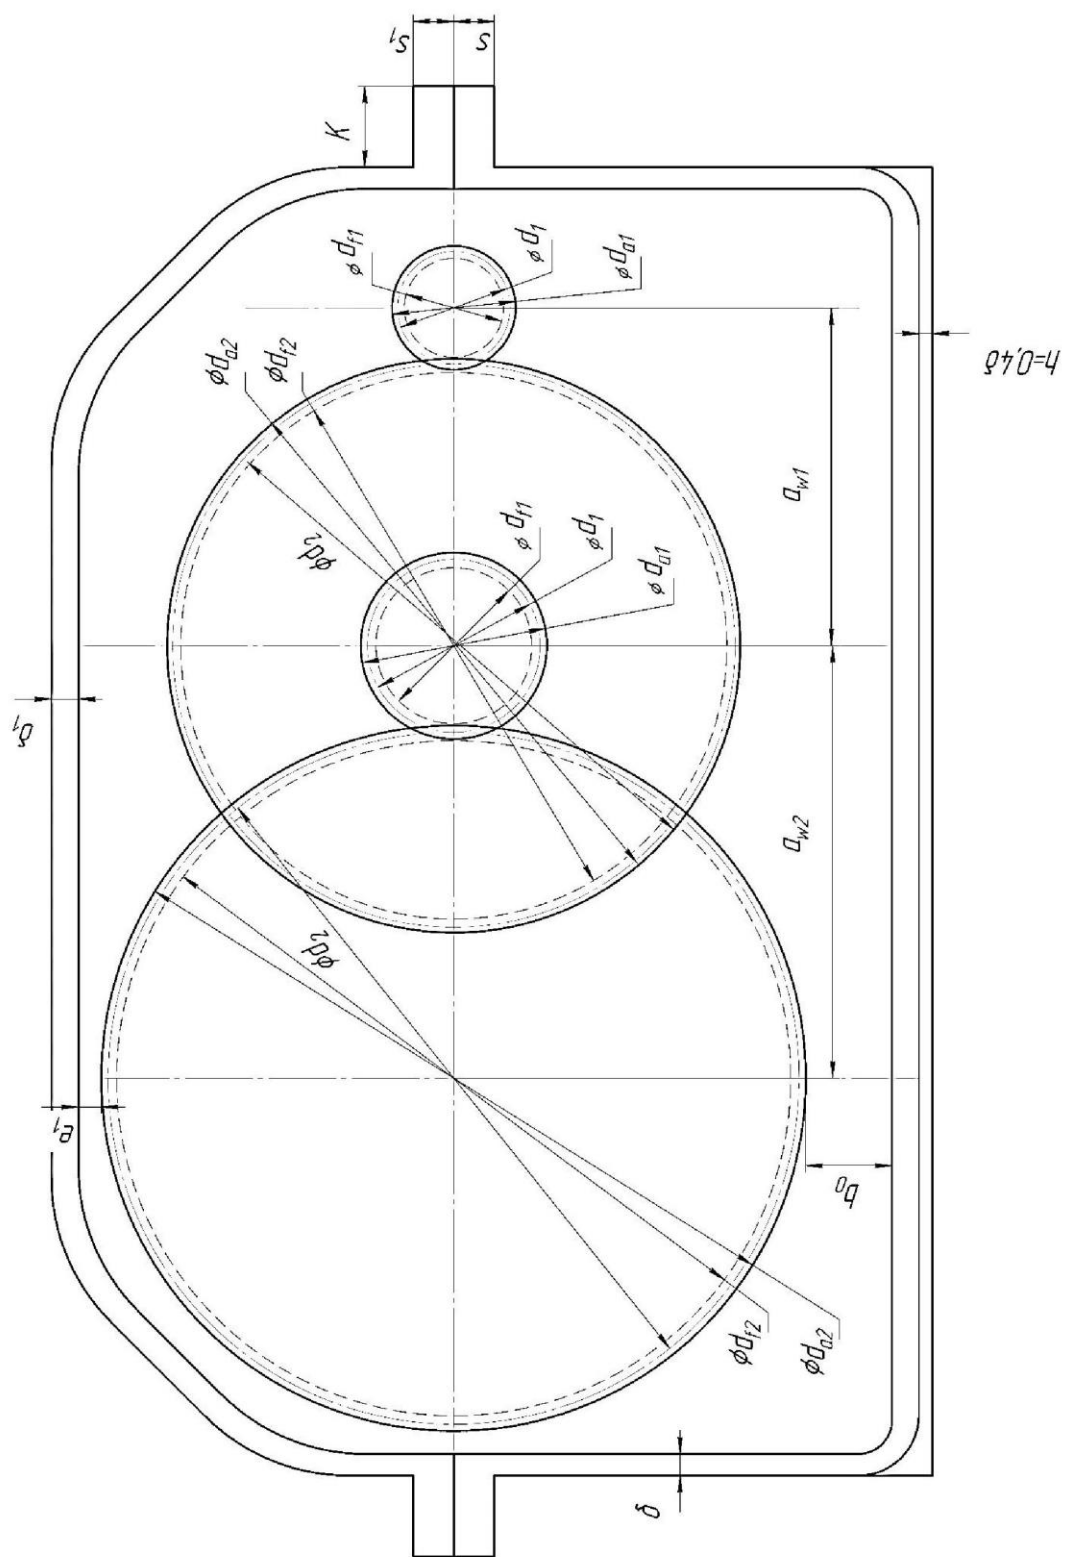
Компонувальне креслення двоступінчастого циліндричного редуктора (початок)
